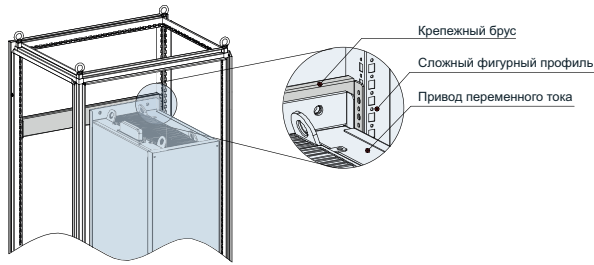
3- мерный вид конструкции T10 - T12 в шкафу
